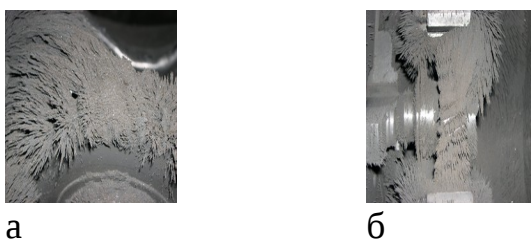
Покрытие сложнопрофильной поверхности детали щеткой из ФАП: а – фронтальный вид; б – общий вид
